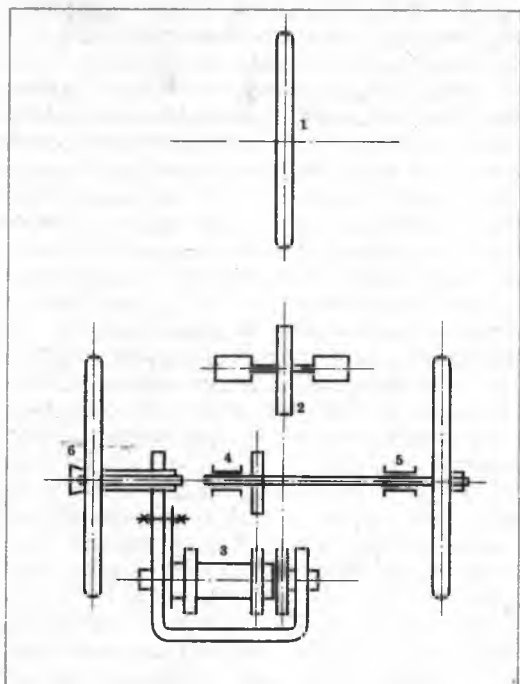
Схема привода трехколесного велосипеда с одной ведущей втулкой: 1 — переднее колесо; 2 — привод на ведомую звездочку заднего колеса; 3 — задняя втулка с дополнительной звездочкой на корпусе; 4 — цепной привод на полуось заднего колеса; 5 — ведущее заднее колесо; 6 — заднее колесо свободного хода
